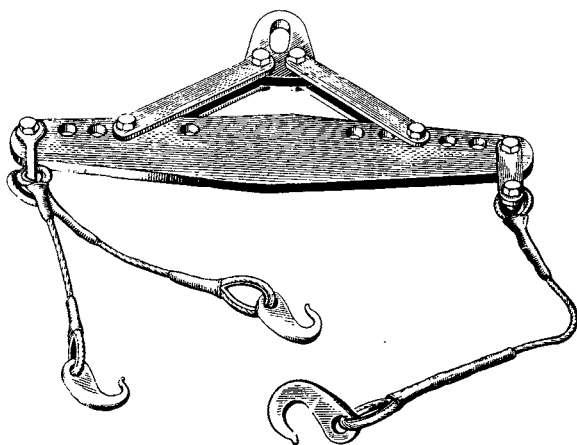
Коромысло 48001-1-010Г для выемки двигателя
